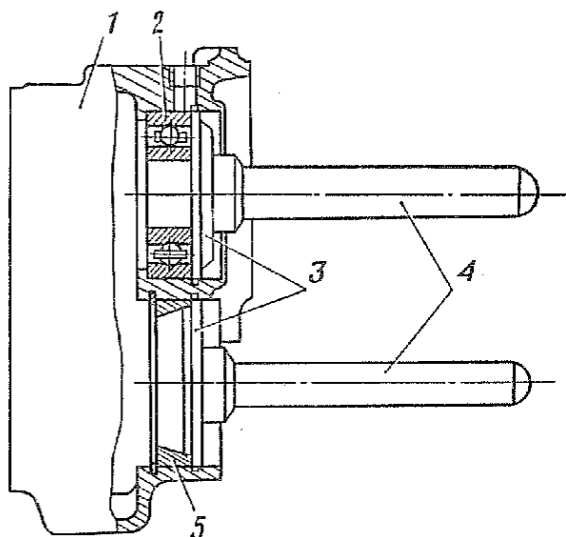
Запрессовка внутренних подшипников колесного редуктора:
